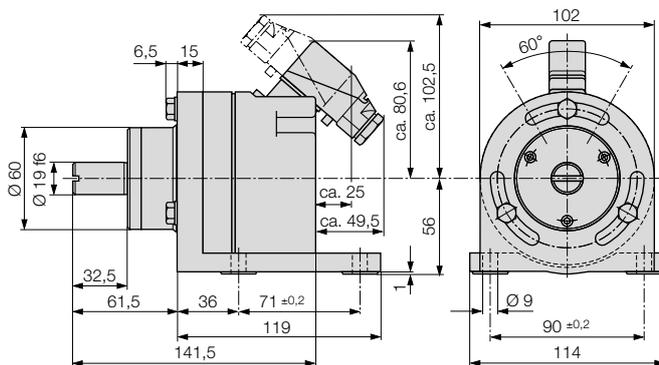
KINAX WT 707 mit Steckverbinder und Fuss.
